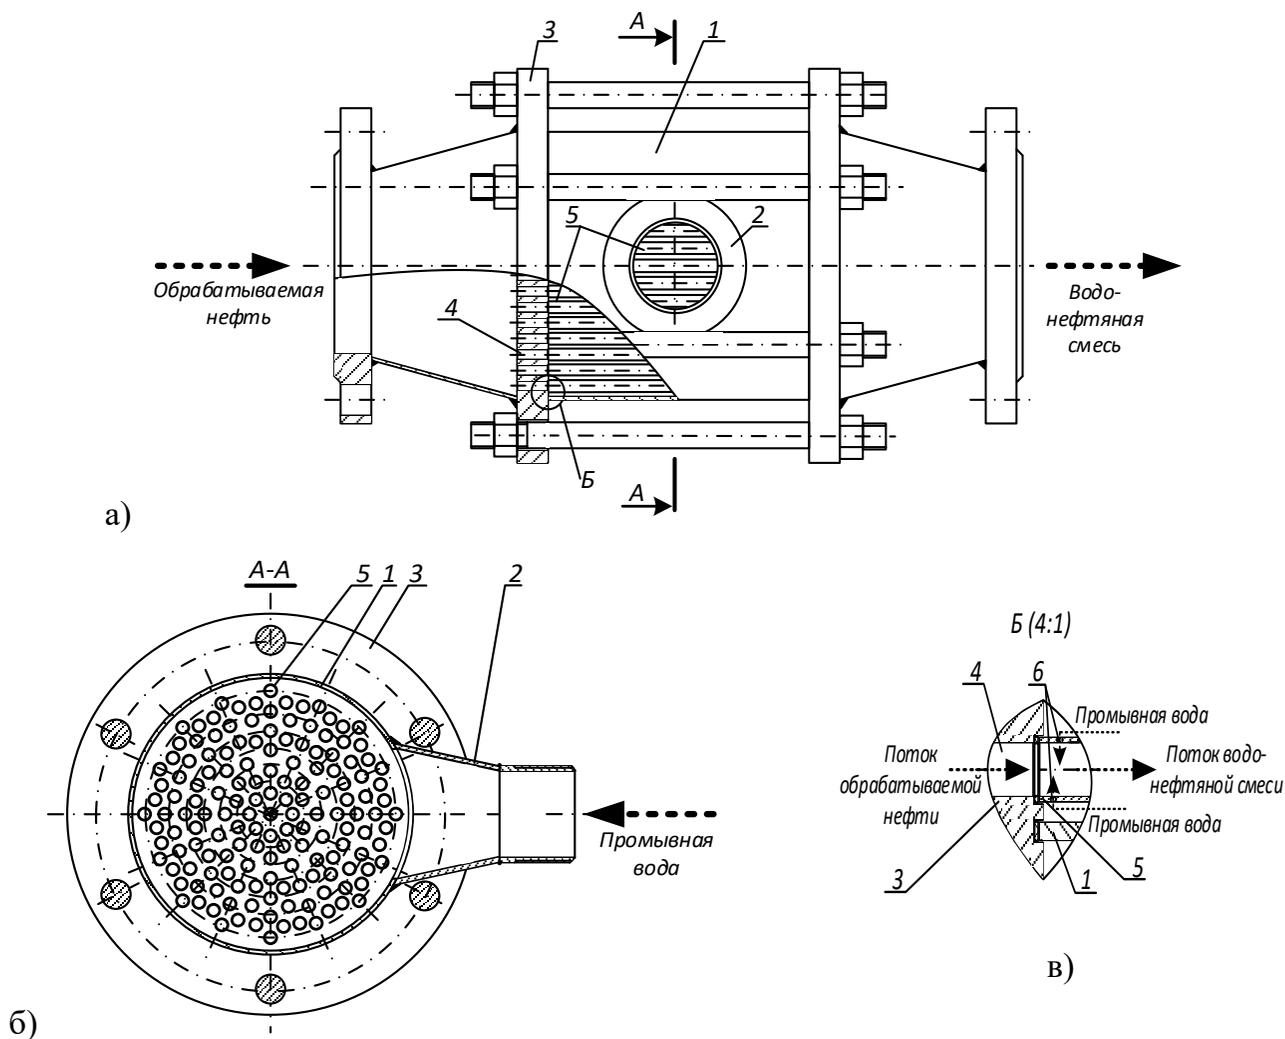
Струеинжекционный смеситель: а–общий вид; б–разрез; в–элемент в масштабе 1 – корпус; 2 – патрубок; 3 – крышки; 4 – отверстия; 5 – трубки; 6 – вводные отверстия
